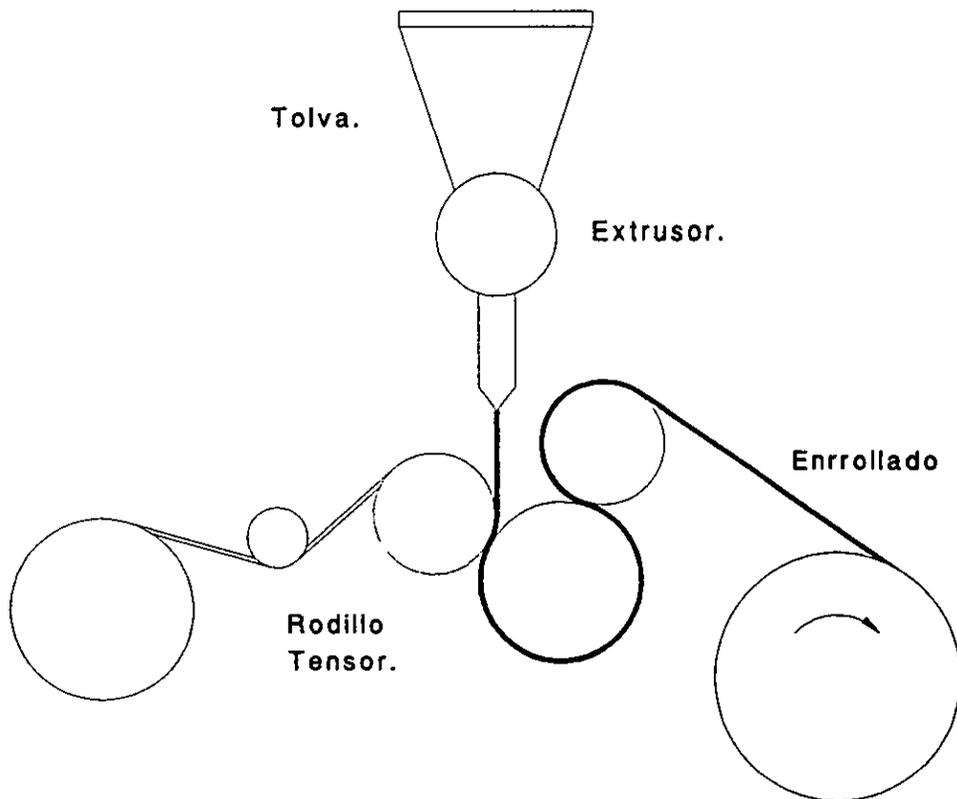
5 Dispositivo para recubrir por extrusión.
